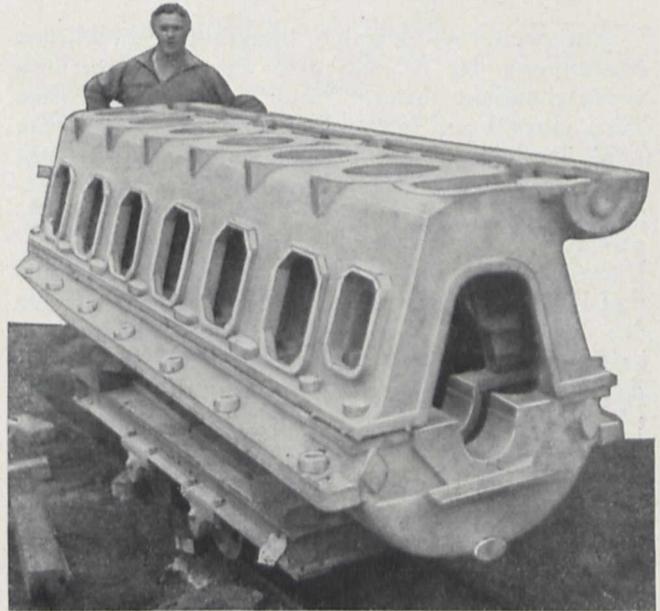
Dieselmotorgehäuse aus 2 Silumingußstücken für einen Zollkutter. Gewicht nur 1050 kg.
